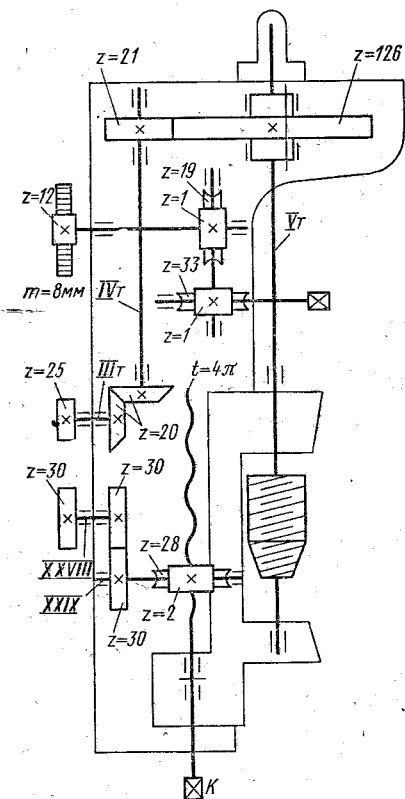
Протяжной суппорт зубофрезерного станка мод. 5345
